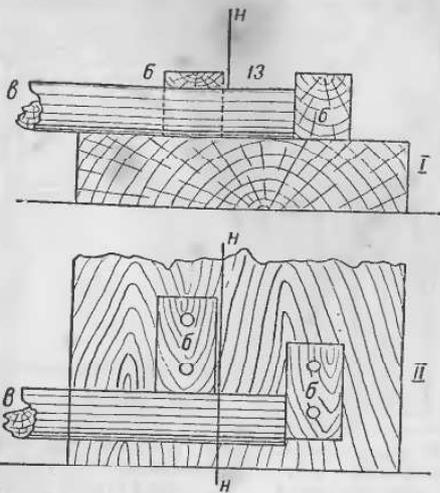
Станок для резки 13-мм разделителей: I — вид сбоку, II — вид сверху, б — брусочки для опоры, н — нож, в — ветка без коры.
